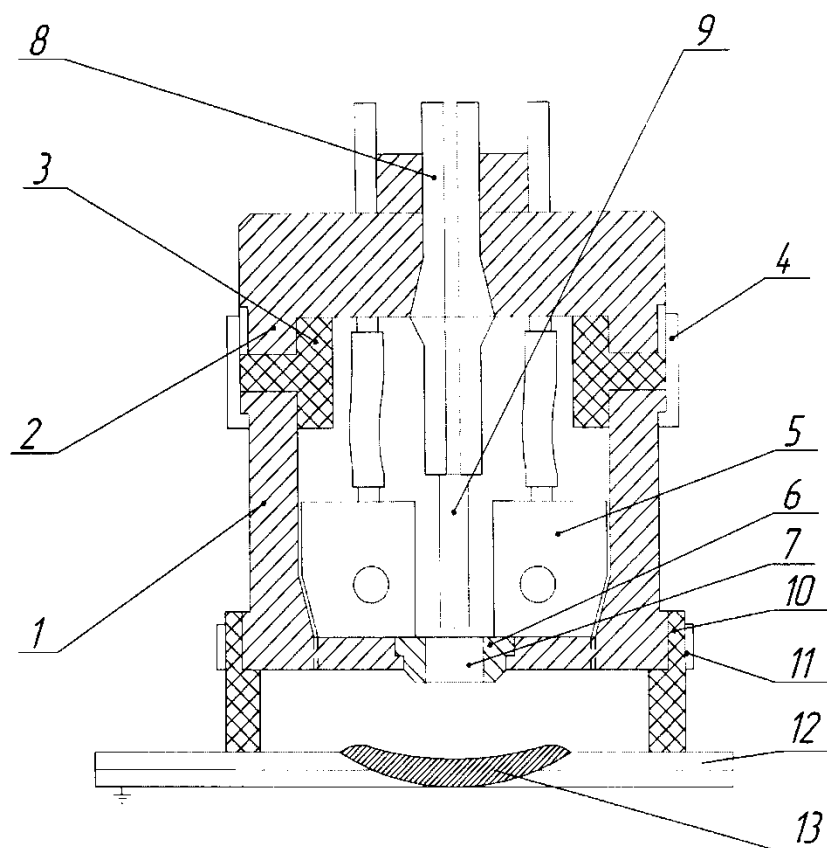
Конструкция плазматрона для точечной плазменной сварки на переменном токе
